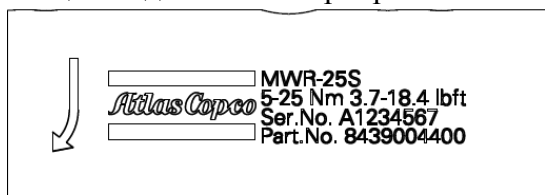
Общий вид типовой маркировки ключей серий MWR-S
